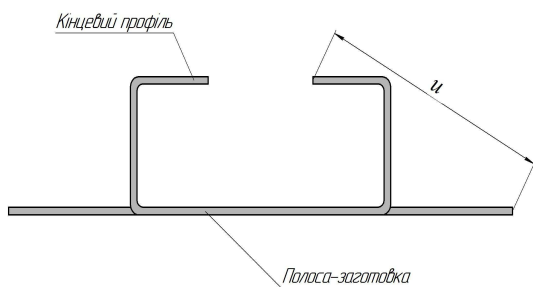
Схема для визначення відстані від краю полоси-заготовки до краю готового профілю
